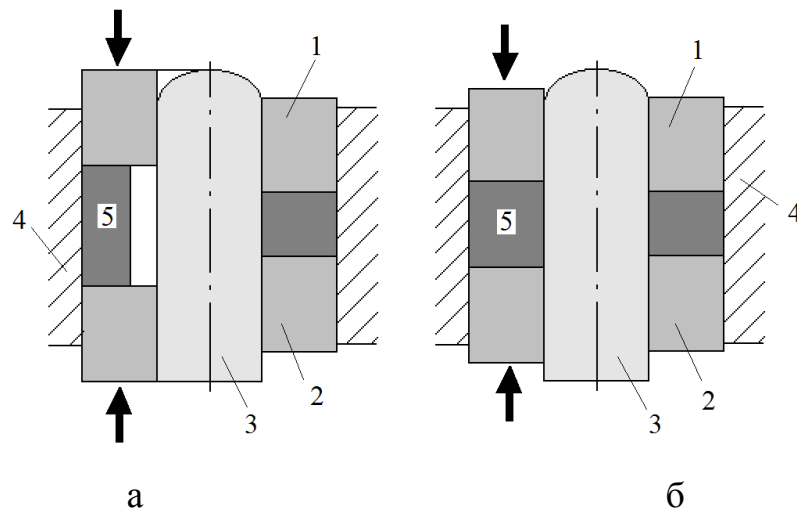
Схеми штампування: а - з радіальною течією до центру; б - допрессовка: 1 - верхній пуансон, 2 - нижній пуансон, 3 - оправка, 4 - матриця, 5 - пориста заготовка
